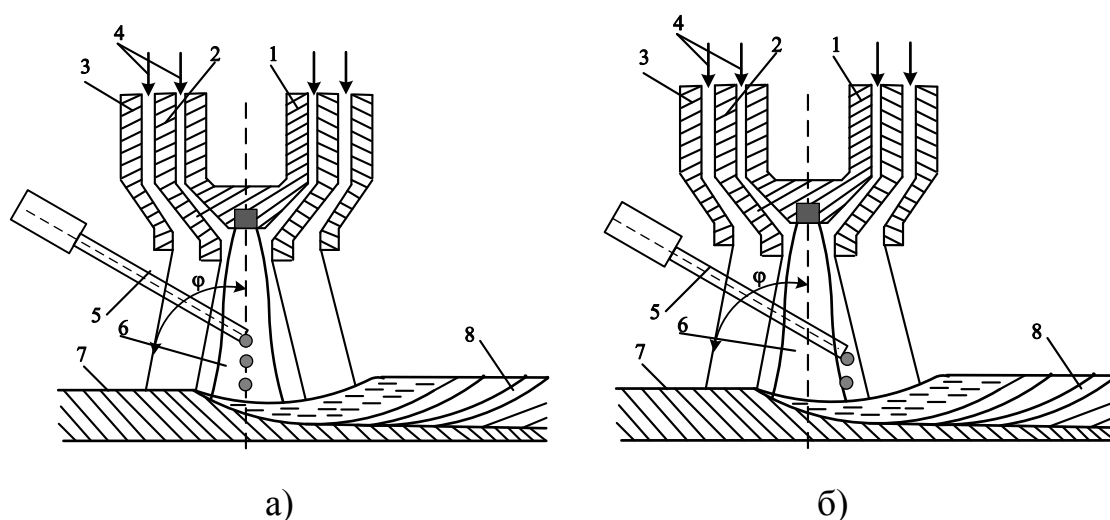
Схемы процесса плазменной сварки в  $CO_2$  при плавлении присадочной проволоки в столбе дуги (а) и на выходе из столба (б): 1 - электрод; 2 - формирующее сопло; 3 - защитное сопло; 4 - плазмообразующий и защитный газы; 5 - присадочная проволока; 6 - дуга; 7 - изделие; 8 - шов
